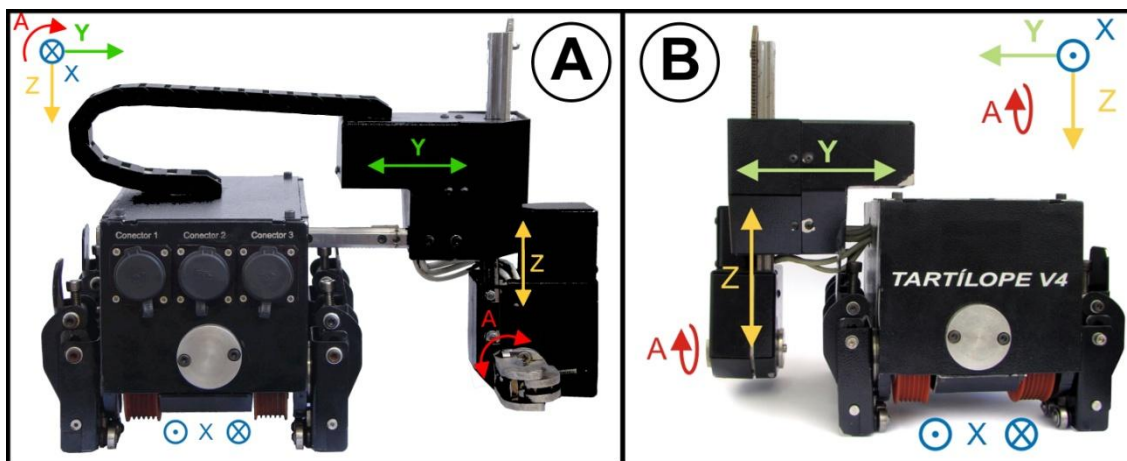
Configurações do Tartilope V4. Em A para soldagem de tubos e em B para soldagem de dutos.
